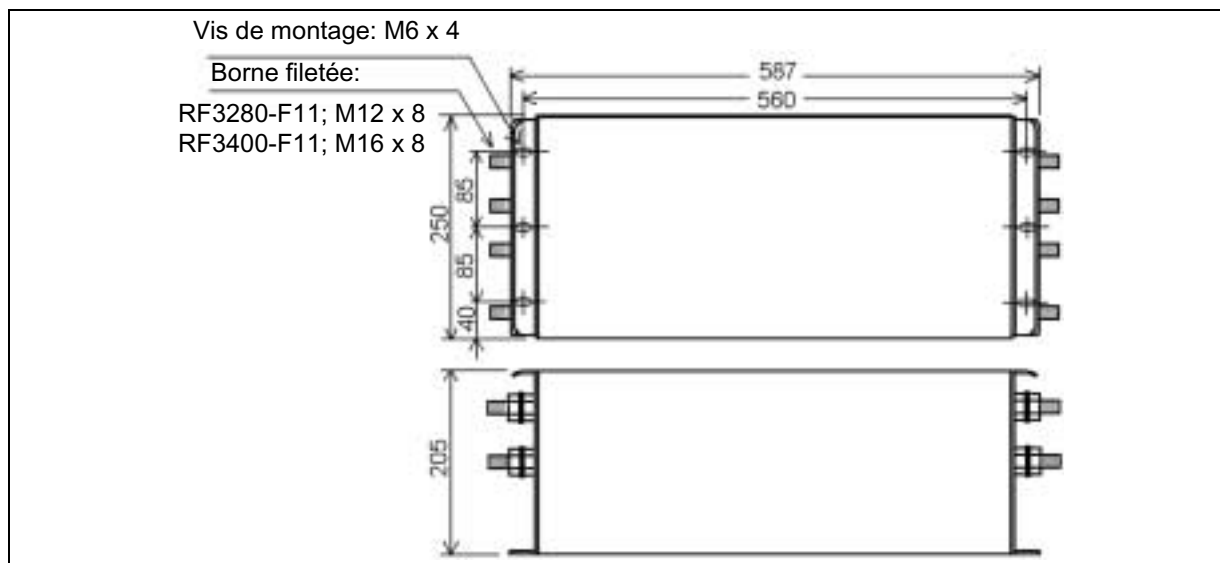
Dimensions externes (RF3280-F11, RF3400-F11)
